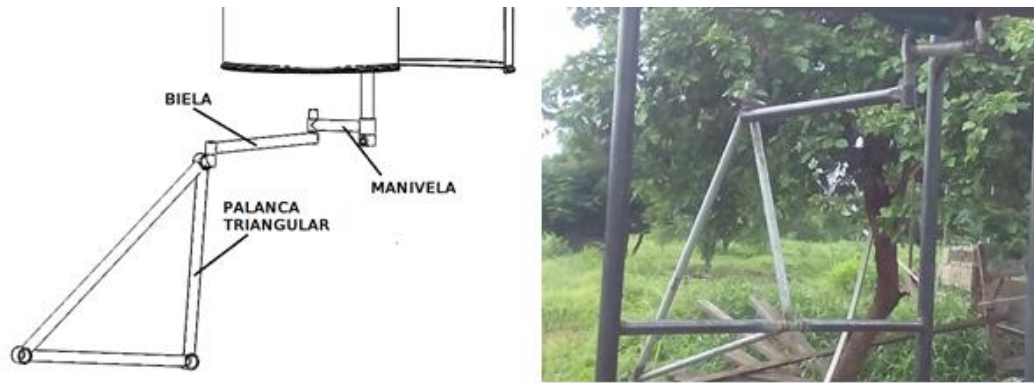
Mecanismo de transformación de movimiento. A la izquierda el modelo diseñado en SolidWorks. A la derecha, el prototipo fabricado.
